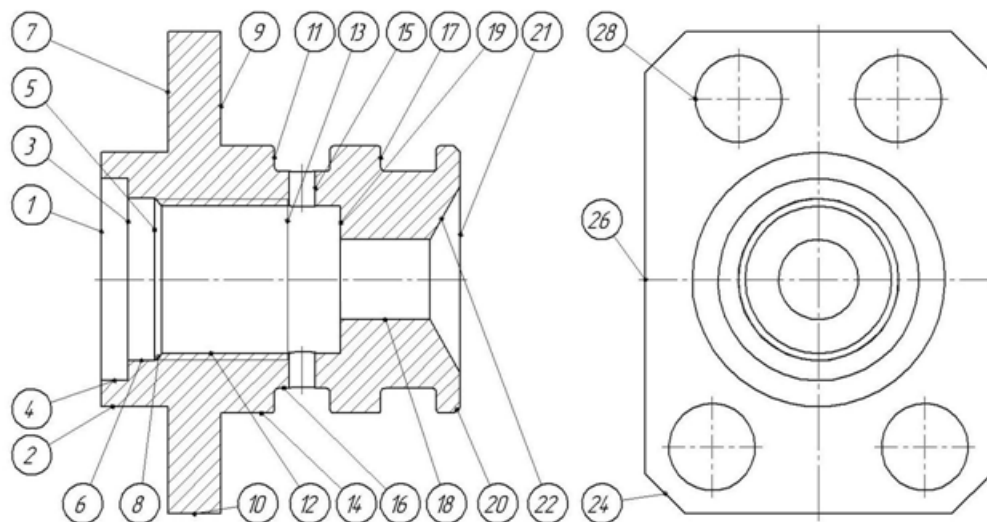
Нумерация обрабатываемых поверхностей детали
